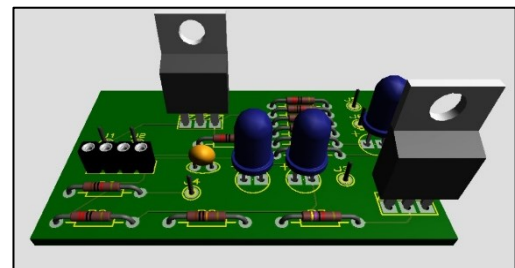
Modelado en 3D de la PCB vista superior. Fuente: Propia
